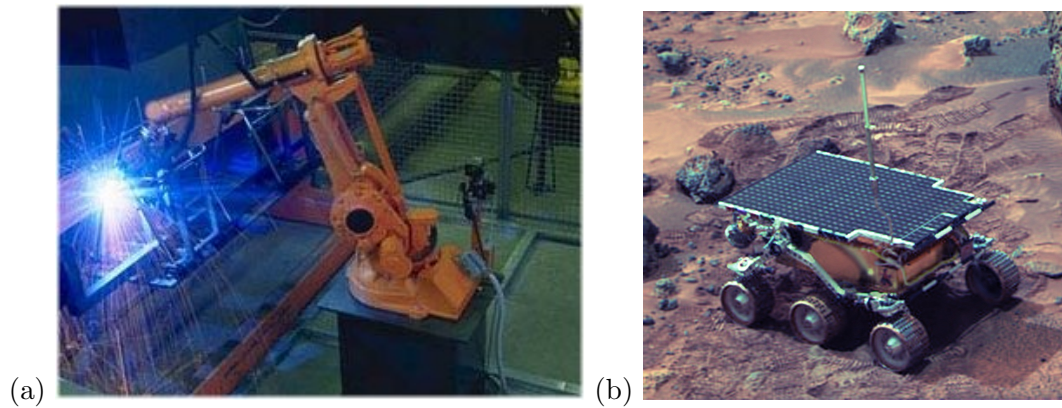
Robot industrial de soldadura (a) y robot Sojourner Rover en Marte (b)
